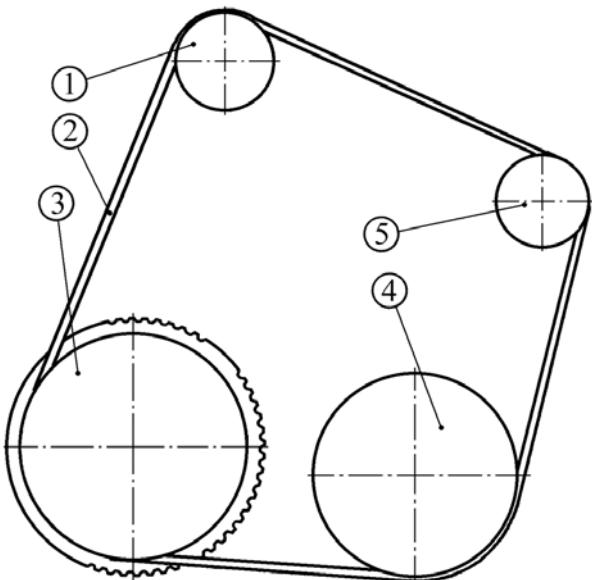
Схема установки ремня привода вспомогательных агрегатов:
